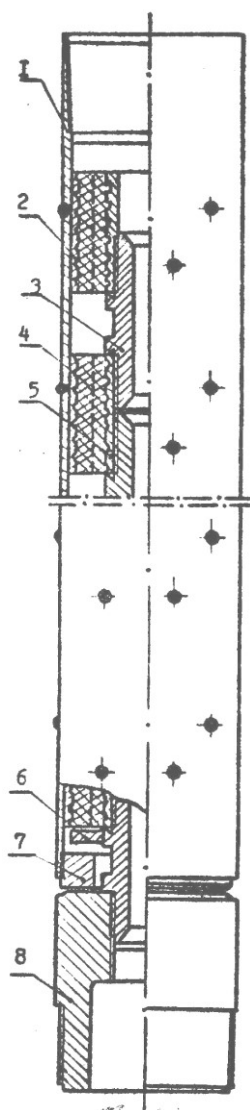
Забійний гумометалевий амортизатор (ЗГМА): 1 – корпус; 2 – зовнішня обойма; 3 – ніпель; 4 – пружний елемент; 5 – внутрішня обойма; 6 – запобіжне кільце; 7 – стопорне кільце; 8 – перехідник
